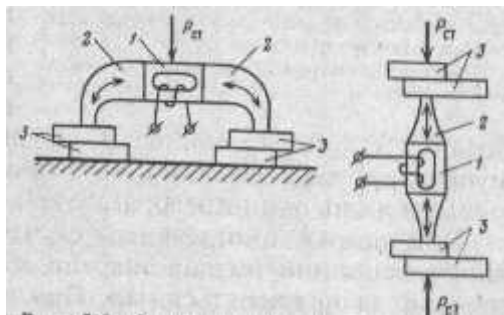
Схемы сварки с двусторонним отбором энергии от преобразователя:
